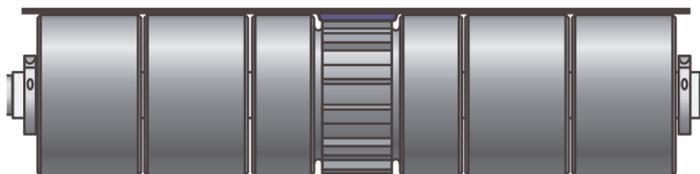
Engranaje apilado/rueda de soporte (engranaje cuadrado de 6 pulg. de ancho)
